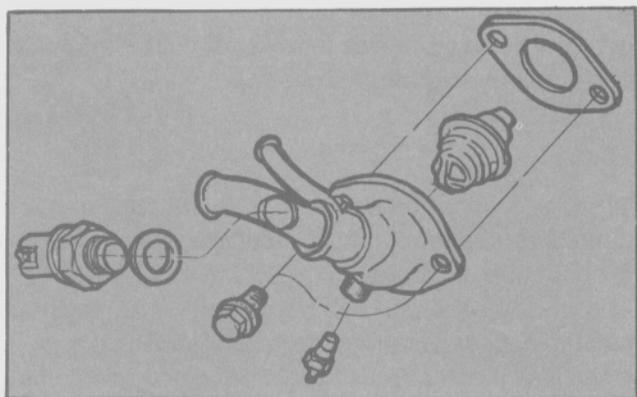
Desmontaje del termostato (Motor I4-2,3L).
